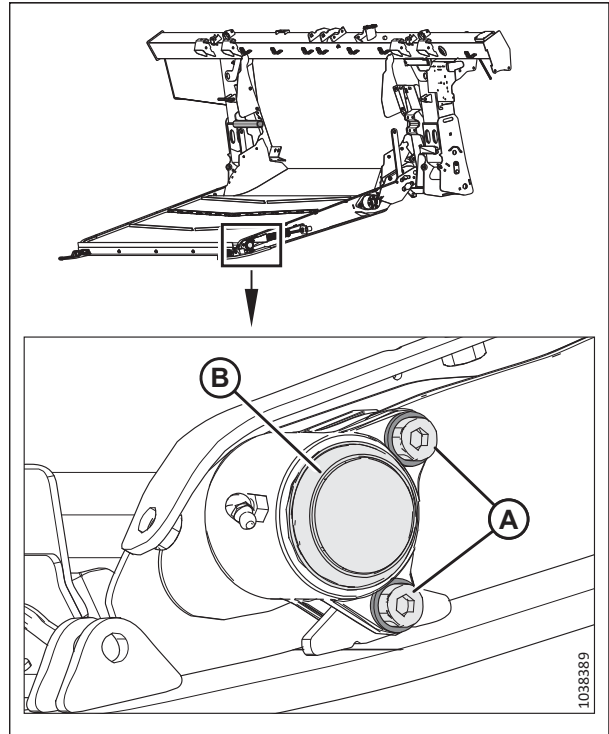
Rodamiento del rodillo tensor: lado izquierdo
